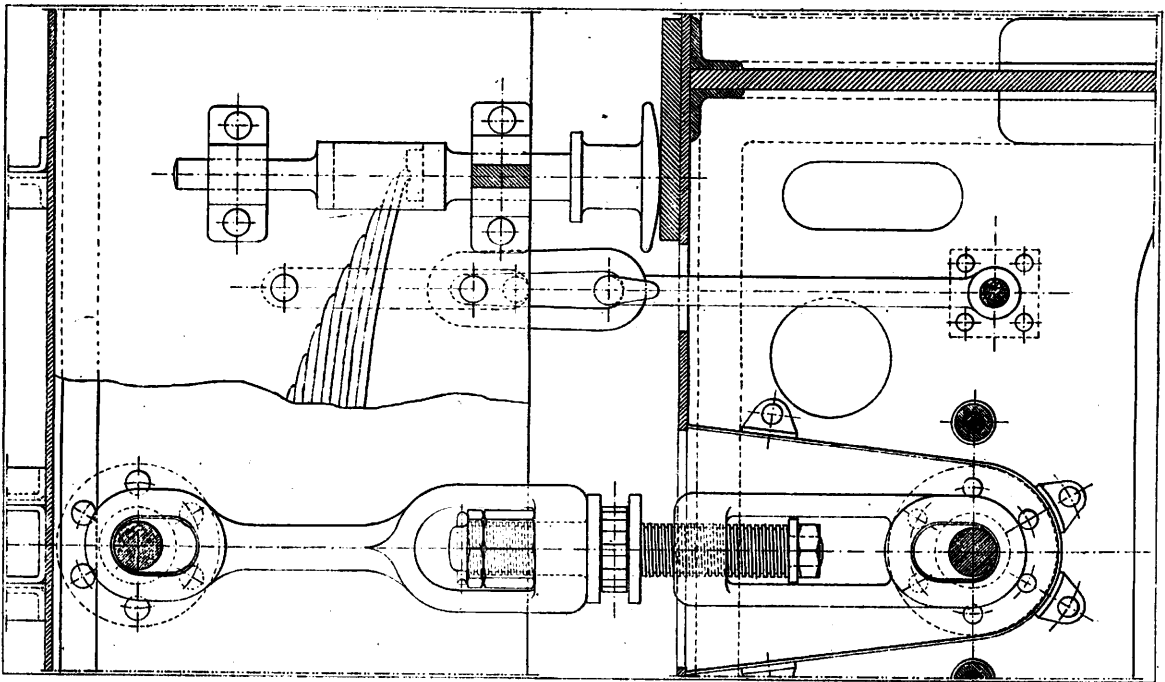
Plan d'attelage de tender, correspondant à la coupe verticale donnée figure 260.
